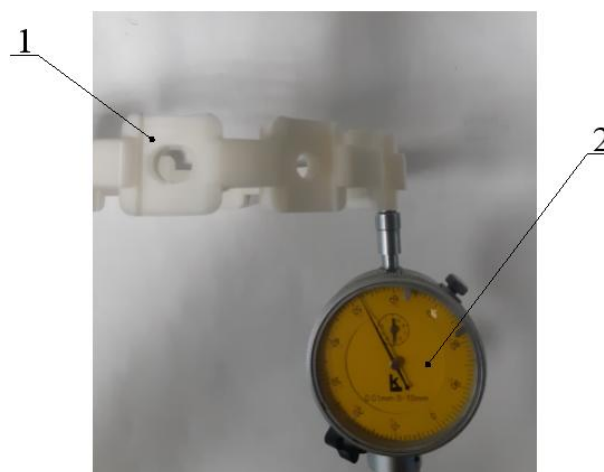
Схема установки на кольцо 1 индикаторной головки 2
